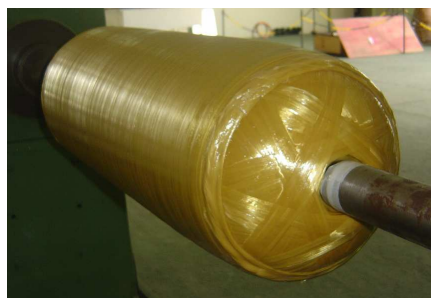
Cilindros leves em fibra de Kveler após processo final de fabricação.
